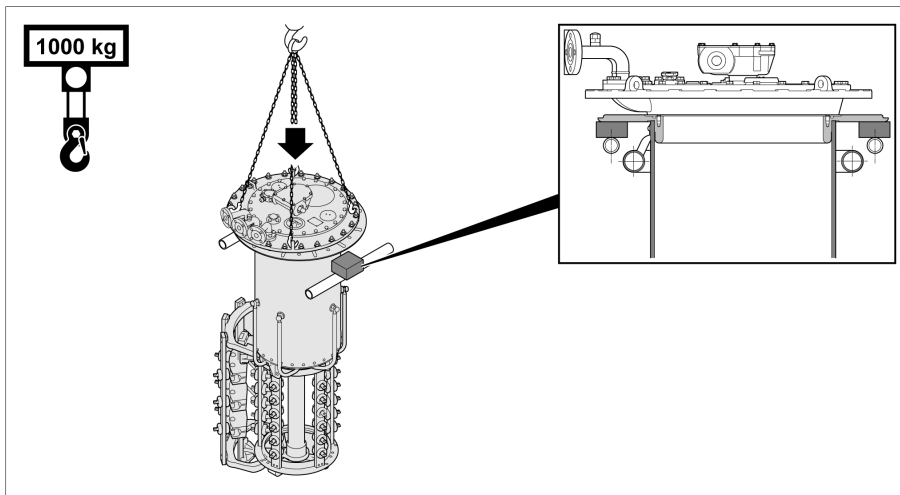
Laststufenschalter mit Distanzstücken auf Tragkonstruktion
